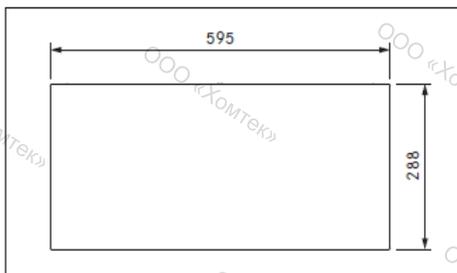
Размеры прибора, модель MSS290, вид спереди
